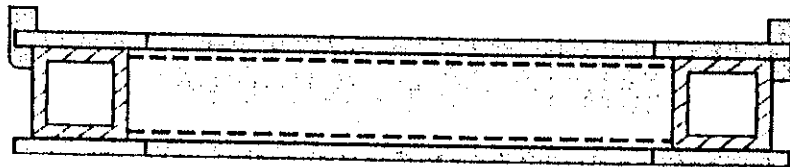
Контроль сварных швов внутренней поперечной балки рамы
